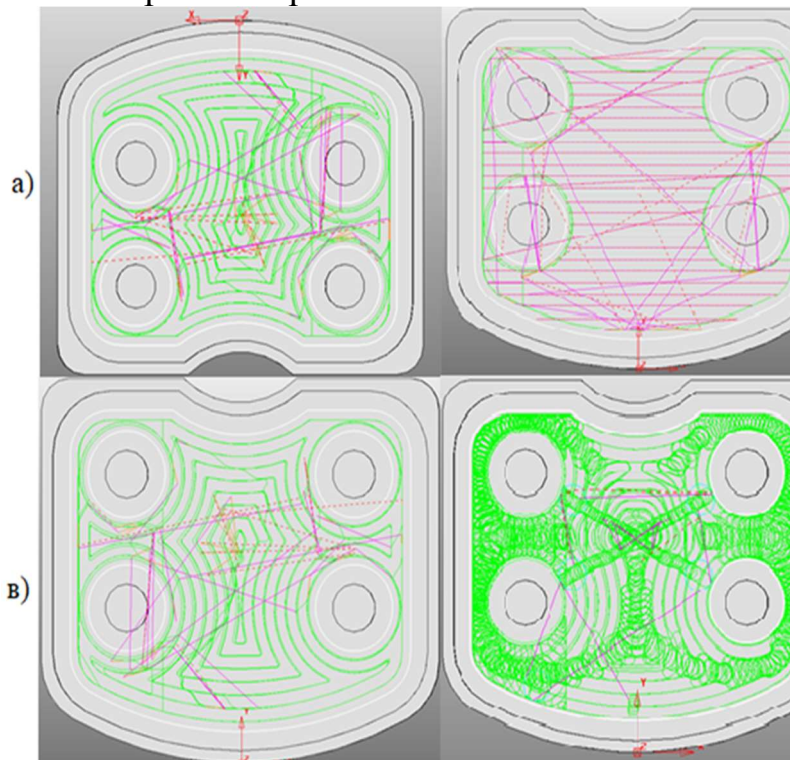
Траєкторії обробки робочої поверхні прес-форми:
